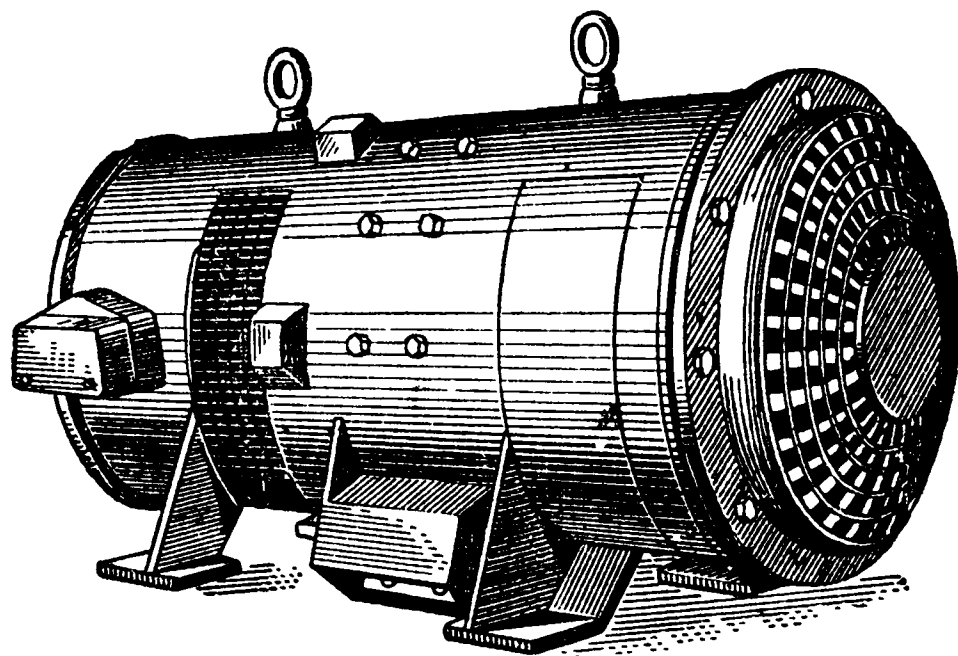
Сварочный агрегат ПСМ-1000
